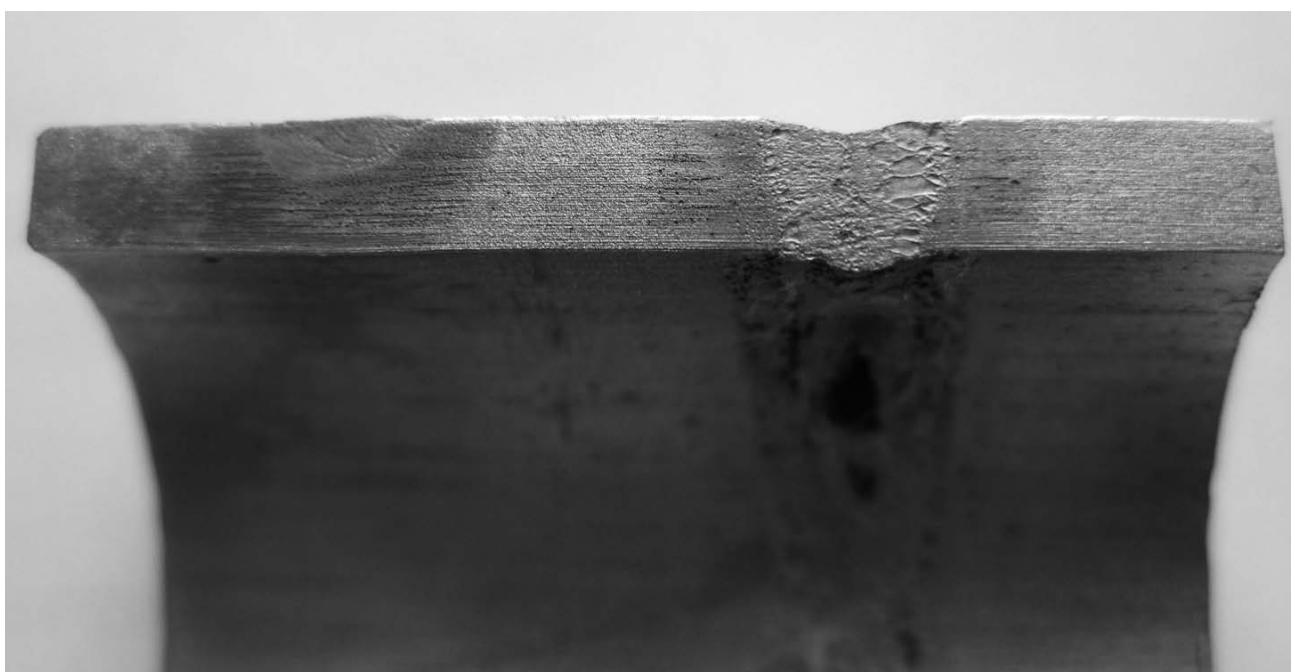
Макроструктура сварного соединения образца – имитатора трубных элементов спиралей ПВД (неповоротных стыков), полученного с помощью автоматической орбитальной гелиодуговой сварки методом автоопрессовки, где слева представлен шов, который сформирован за один проход автоматической орбитальной гелиодуговой сваркой методом автоопрессовки, а справа – шов, сформированный автоматической орбитальной аргонодуговой сваркой тем же методом
